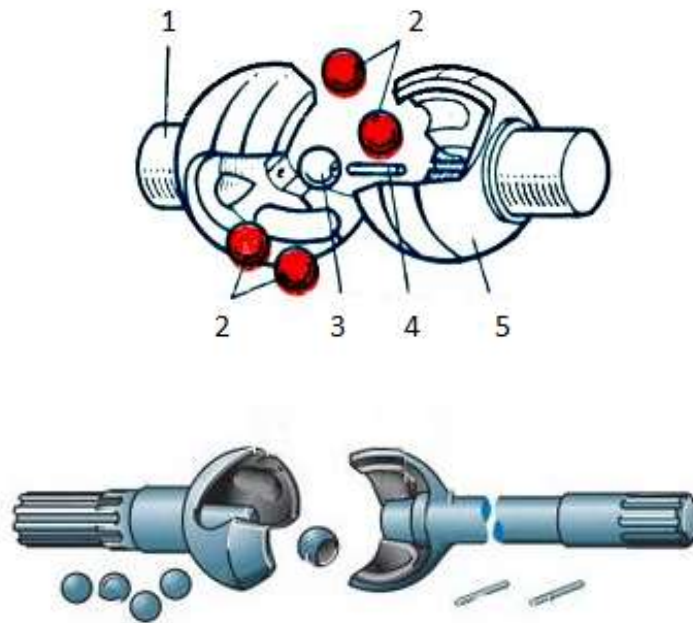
Кульковий шарнір з ділительними канавками типу «Бендікс-Вейсс» [6]: 1 – ведучий вал; 2 – кульки; 3 – центрувальна кулька; 4 – центрувальний штифт; 5 – ведений вал
